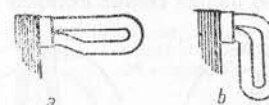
Bobinaj în manta (a) și bobinaj frontal (b).
